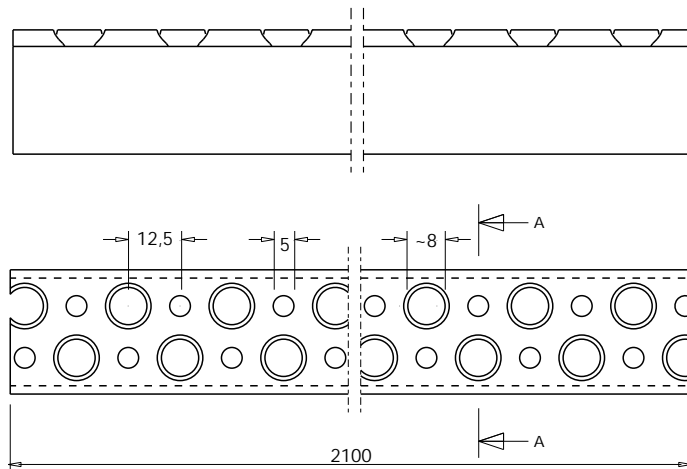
Vista planta y vista de frente de peldaño de escala.
